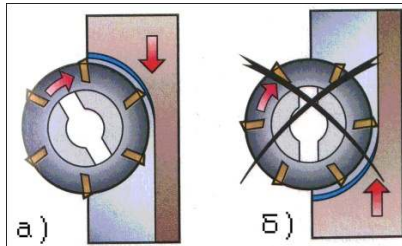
Направление фрезерования: а – попутное; б – встречное
